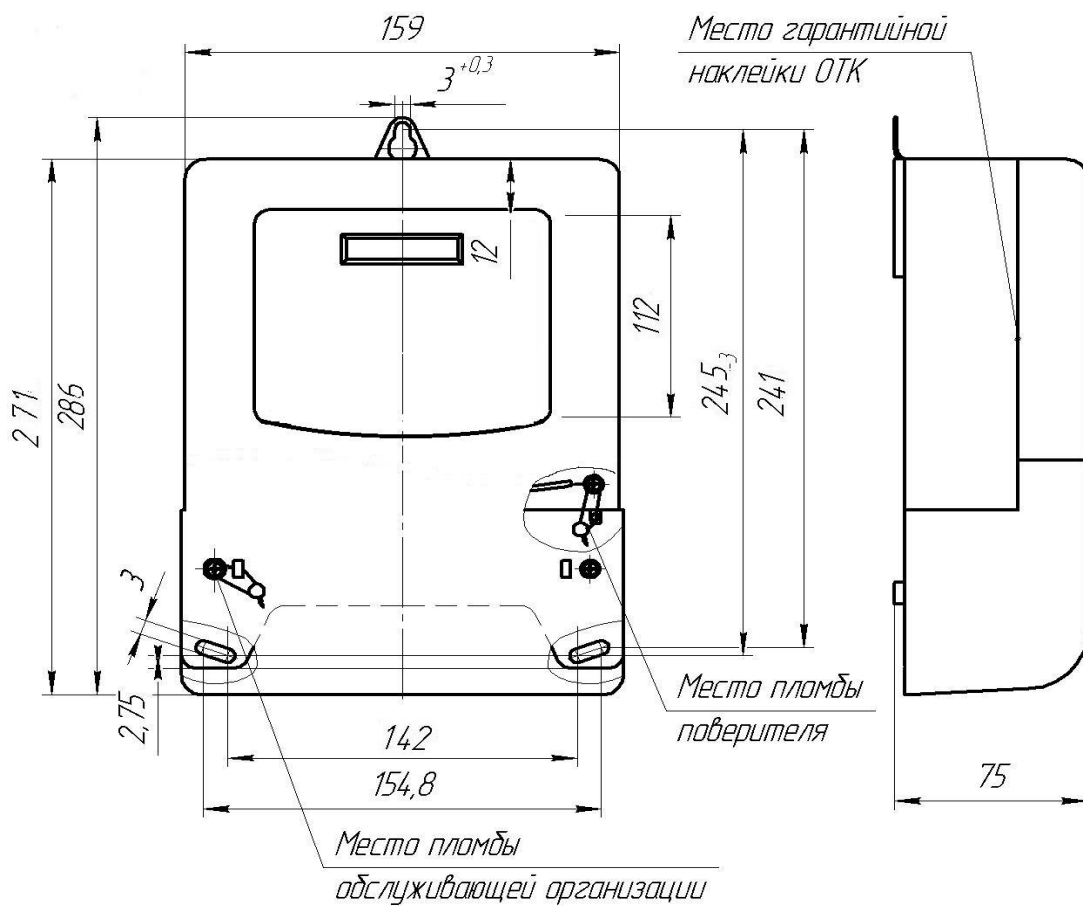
Общий вид счетчика в корпусе Н7/Н11
